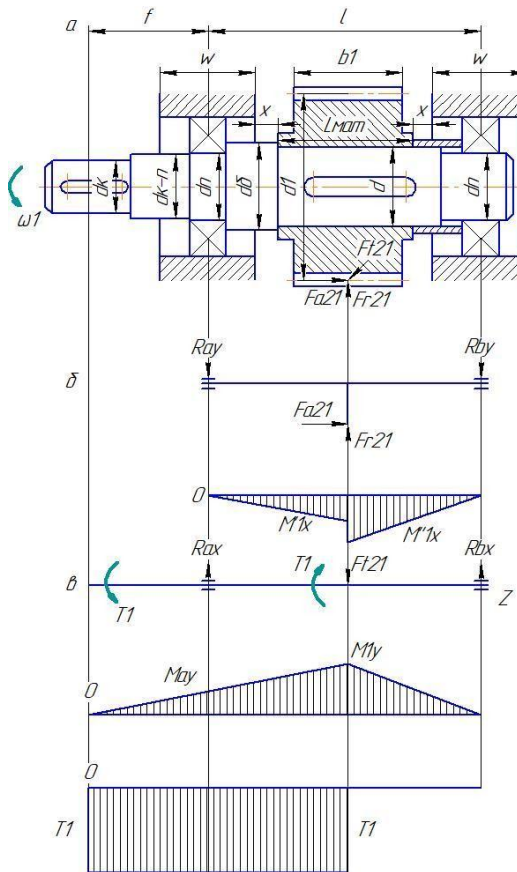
Схема ведучого вала циліндричного косозубого редуктора
